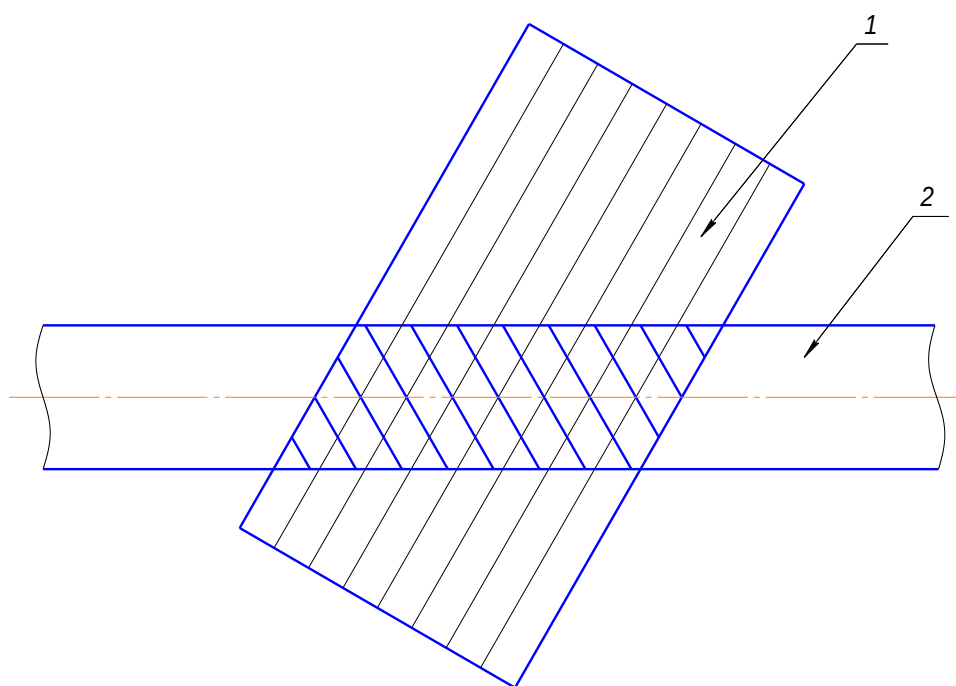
Радиально-осевой способ накатывания: 1 – ролик с кольцевой нарезкой; 2 – обрабатываемая деталь
